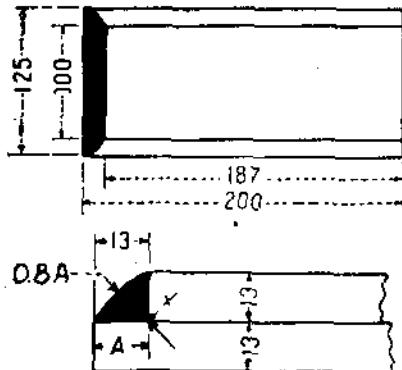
Образец для испытания сварки внахлестку.
